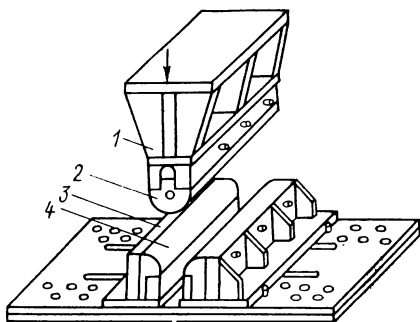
Универсальный штамп для холодной гибки листов под прессом. 1 — пуансонодержатель; 2 — сменный пуансон; 3 — матрицедержатель; 4 — сменные матрицы.
